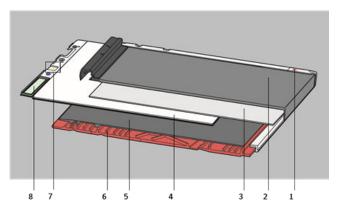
Vista detallada de la etiqueta de placa y chasis del CR MM3.xR Mammo
